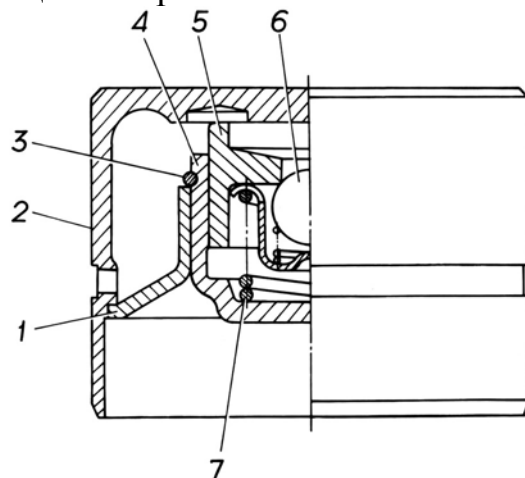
Гидротолкатель: 1 - направляющая втулка компенсатора; 2 - корпус гидротолкателя; 3 - стопорное кольцо; 4 - корпус компенсатора; 5 - поршень компенсатора; 6 - обратный шариковый клапан; 7 - пружина
